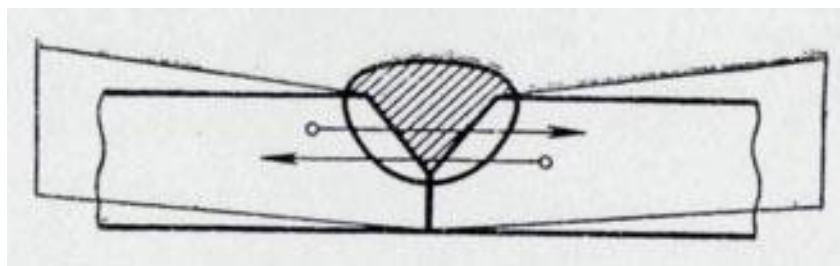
Деформация при сварке стыкового соединения (угловая)
